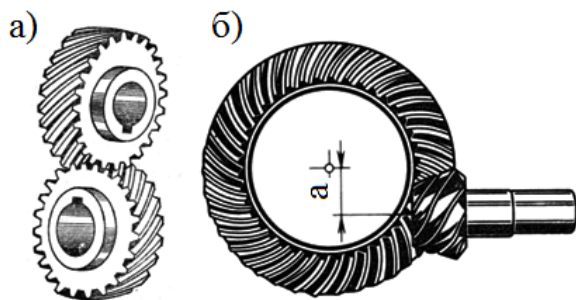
Передачи для перекрещивающихся осей валов: а) винтовыми колёсами; б) гипоидная передача.
